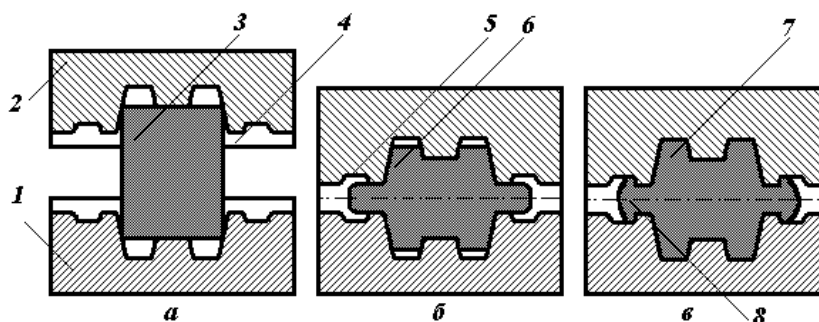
Открытая штамповка: а, б, в – начальный, промежуточный и конечный моменты штамповки; 1 – нижняя часть штампа; 2 – верхняя часть штампа; 3 – заготовка; 4 – канавка для облоя; 5 – магазин; 6 – промежуточная поковка; 7 – поковка; 8 – облой
